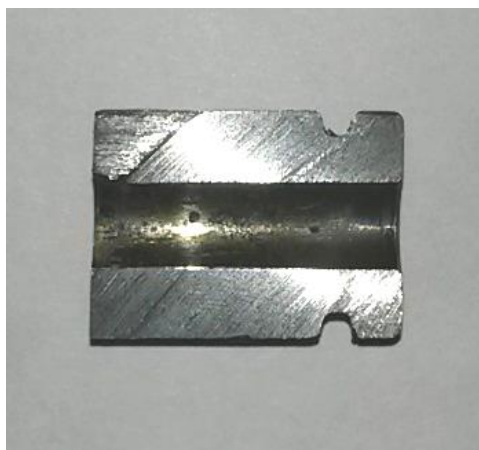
metà cilindretto derivante da una sezione longitudinale
